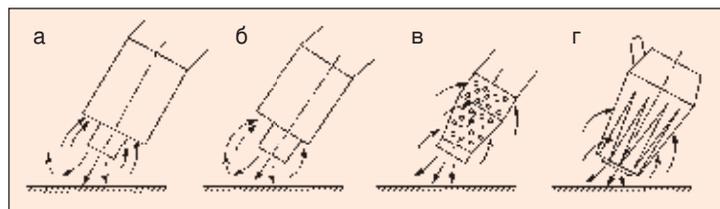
Схемы аспирационных устройств к горелкам для механизированной сварки в защитных газах: а — цилиндрическое коаксиальное; б — цилиндрическое аксиальное; в — коническое дырчатое; г — конусно-щелевое
